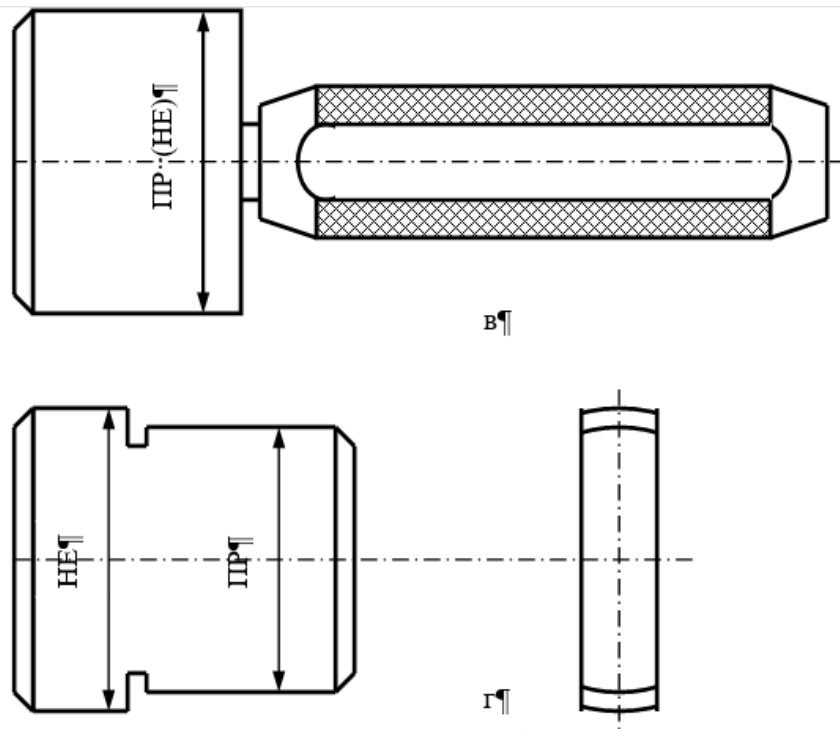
Схема вимірювання деталей гладкого циліндричного з'єднання гладенькими предільними калібрами
